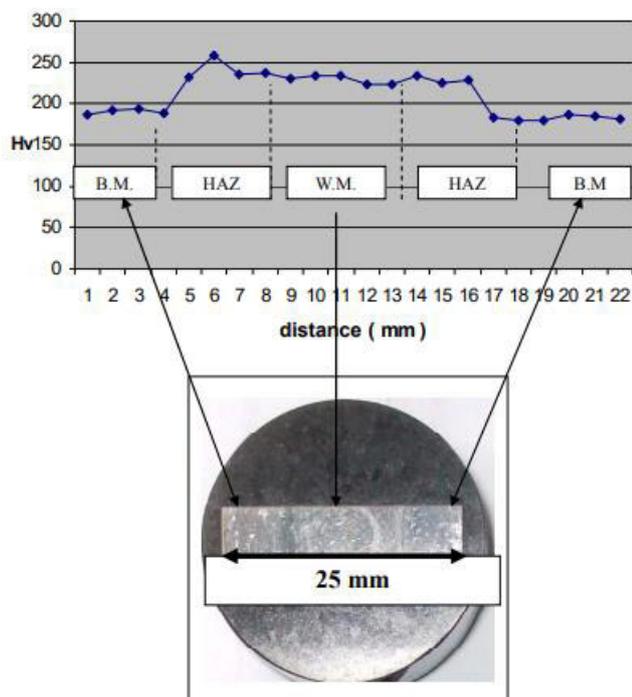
Измерения твердости от основного металла до металла сварного шва
